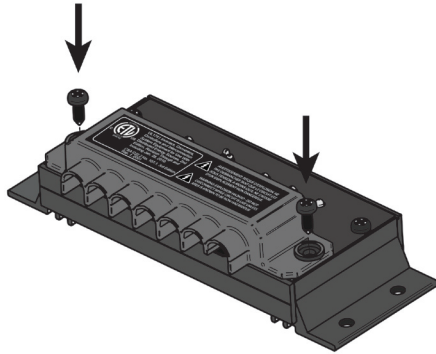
Befestigen der Klemmenblende mit 2 Schrauben.
